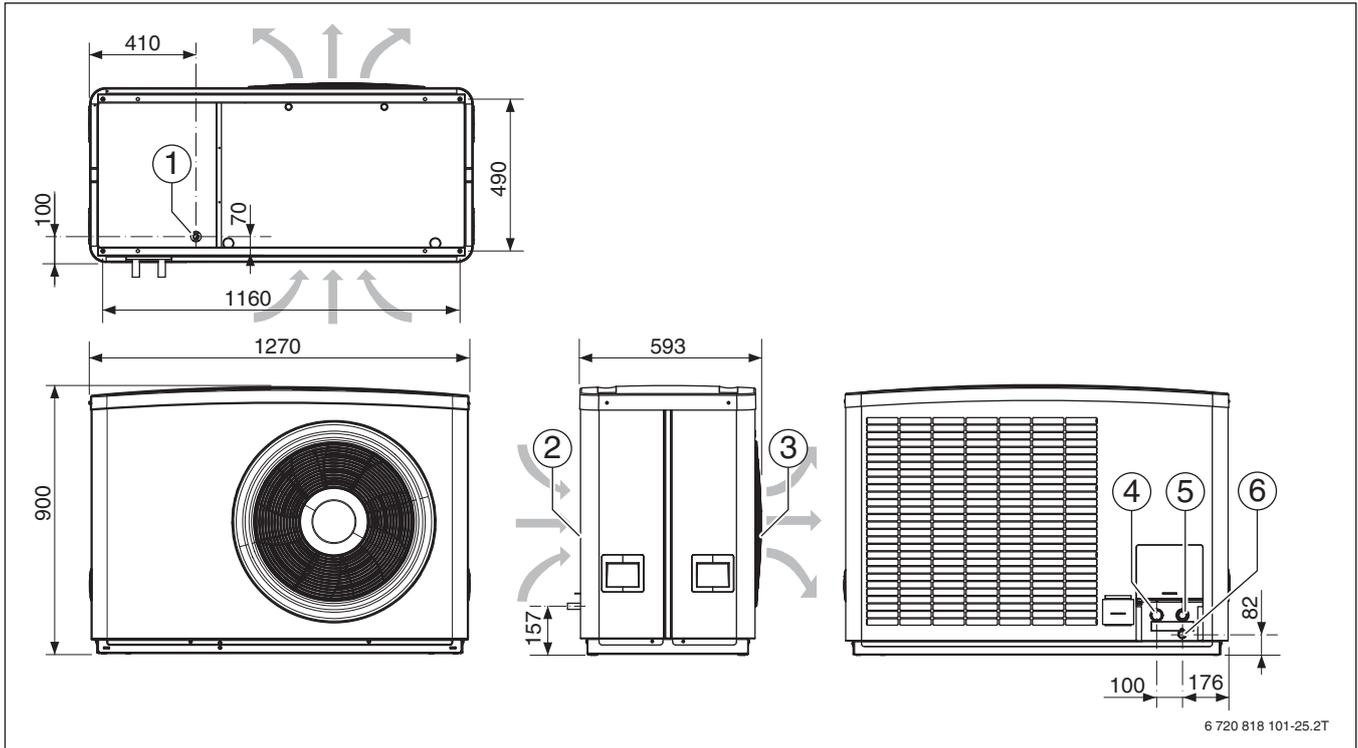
Abmessungen und Anschlüsse ODU W9 HT
